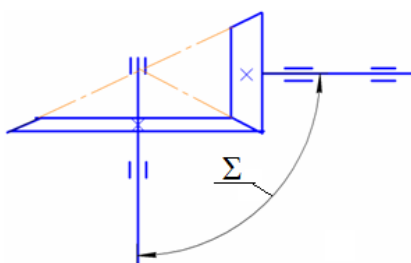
Кинематическая схема конической передачи. Рис.4.14. Поверхности конического колеса.
